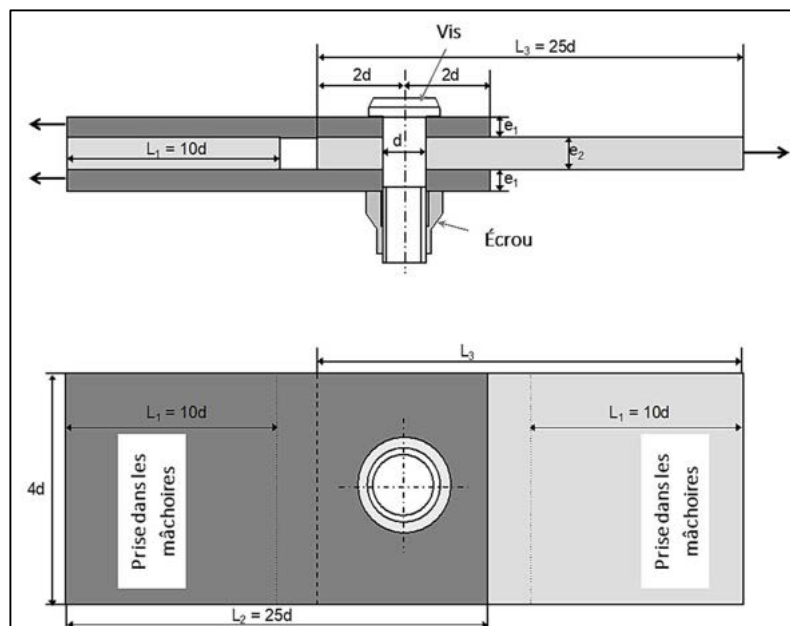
Dimensions des éprouvettes d'essais de fatigue avec fixation
